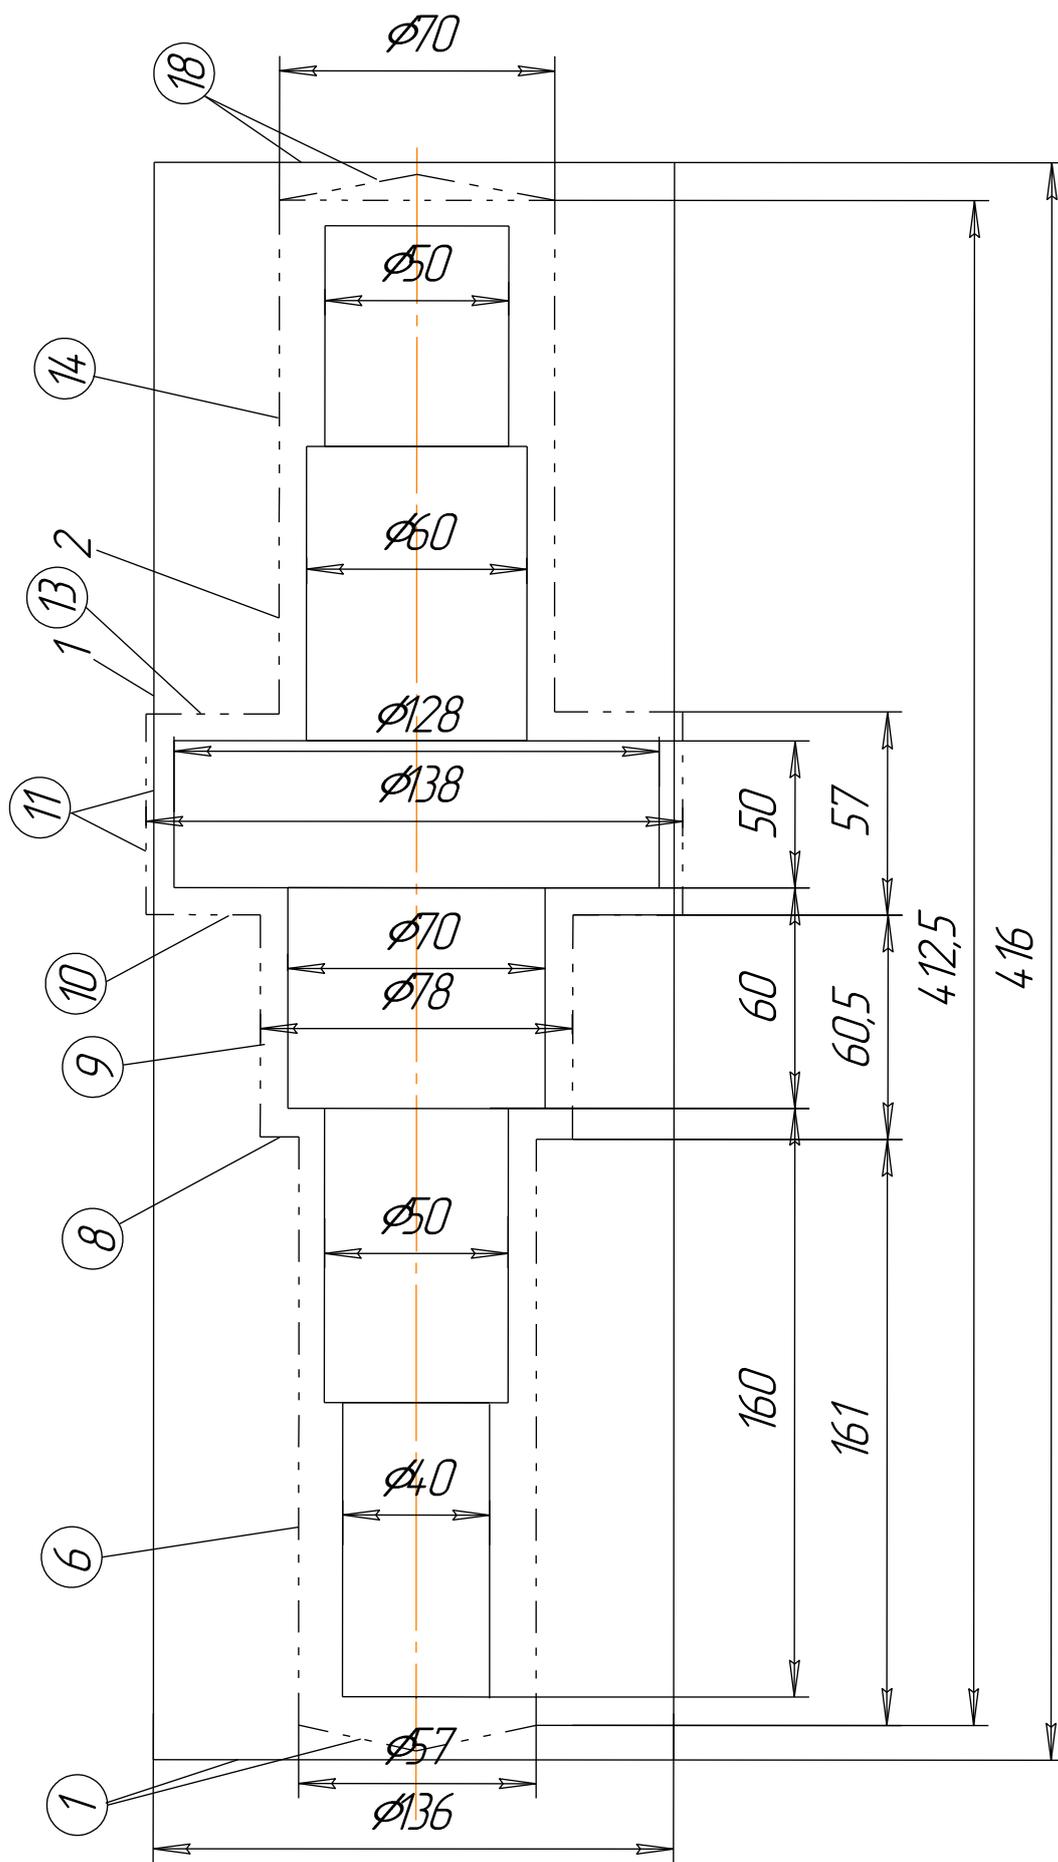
Контур заготовки: 1 – прокат, 2 – штамповка
